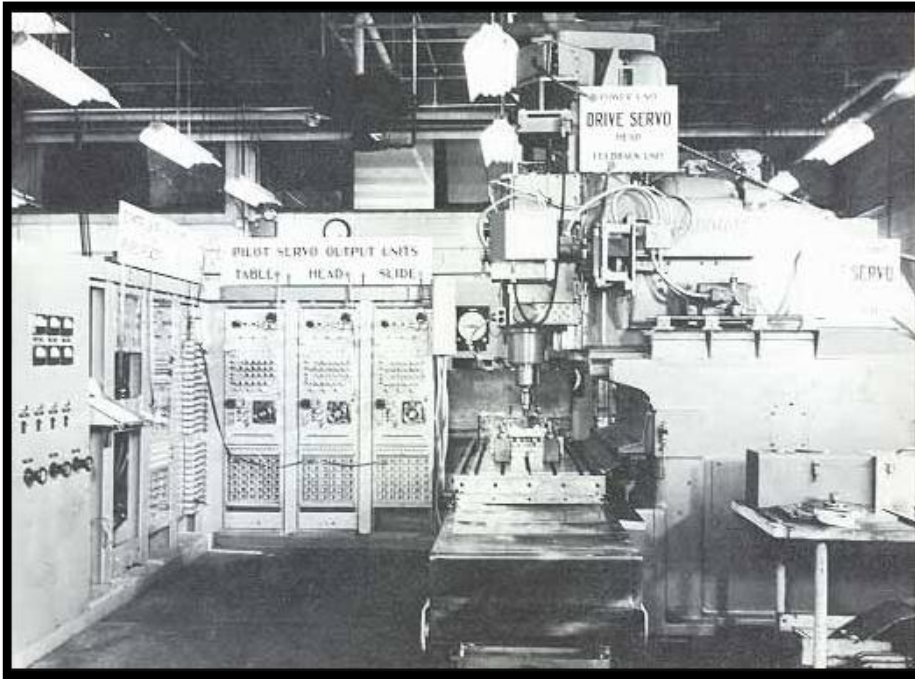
La fraiseuse à commande numérique originale de 1952 du MIT était une machine Cincinnati Milling Machine Company Hydro-Tel à 3 axes modifiée.
